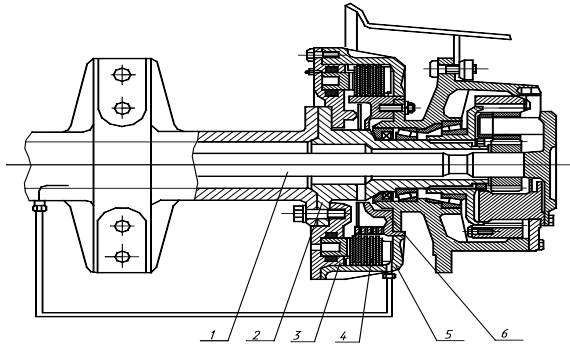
Гальмівний механізм з примусовою циркуляцією оливи японської фірми «Акебоно букеки коге К.» [10]: 1 – напіввісь; 2 – маточина; 3 – корпус; 4 – пакет обертових і нерухомих фрикційних дисків; 5 – затиск корпусу; 6 – лопаті для створення примусової циркуляції оливи
